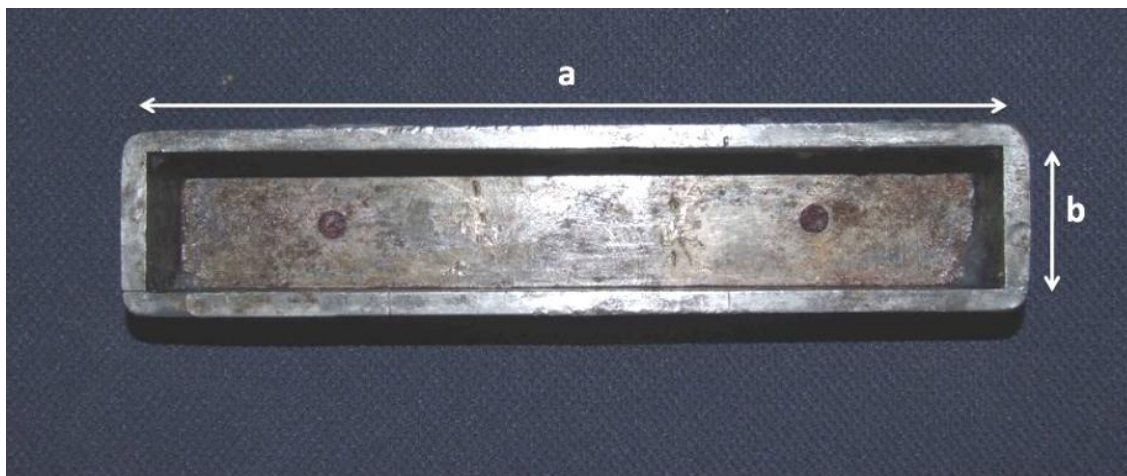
Molde em metal para inclusão das hemimandíbulas – vista superior. (a) Comprimento do suporte = 18 cm, (b) Largura do suporte = 3cm.
